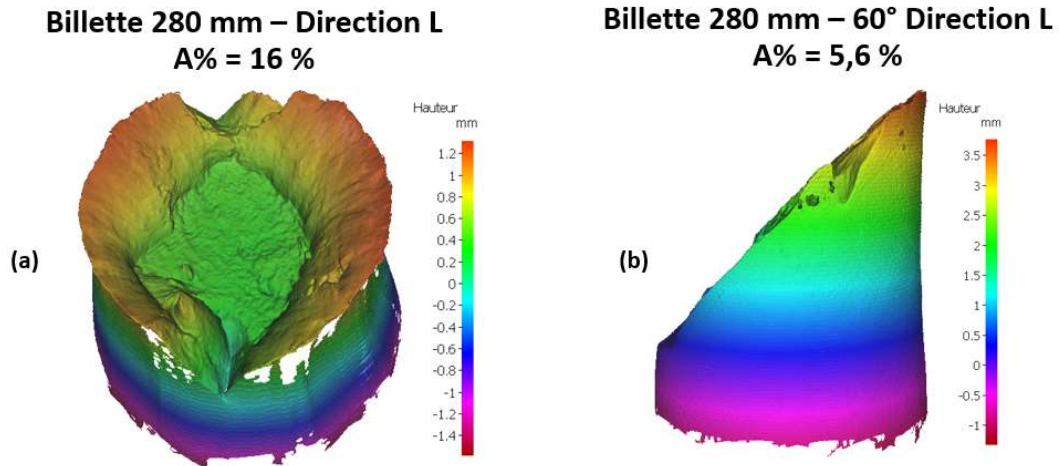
Reconstruction 3D à l'aide d'un microscope optique de deux faciès de rupture d'éprouvettes conventionnelles avec des géométries différentes. L'éprouvette (a) a été prélevée dans la direction L de la billette de diamètre 280 mm. L'éprouvette (b) a été prélevée à 60° de la direction L dans le plan LT de la billette de diamètre 280 mm.
